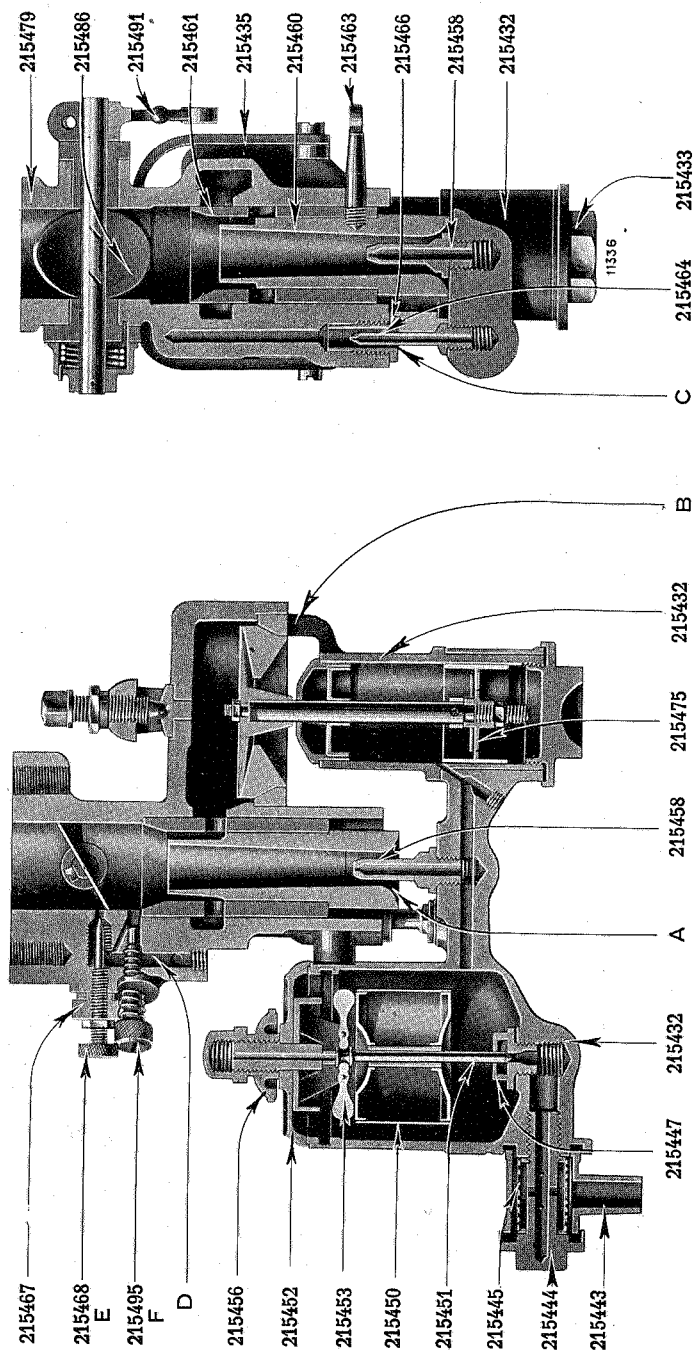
Le carburateur. Coupes longitudinale et transversale.
